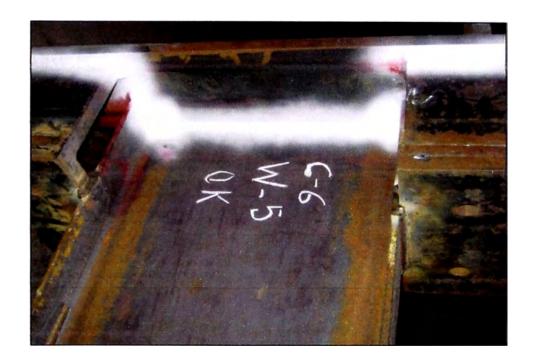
In pección de pase acabado en columnas C-6, soldador w5.
